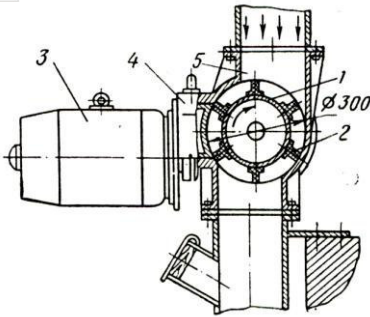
Комірковий живильник з регульованим приводом: 1-ротор; 2-гнучкі лопаті; 3-електродвигун; 4- редуктор; 5- корпус
